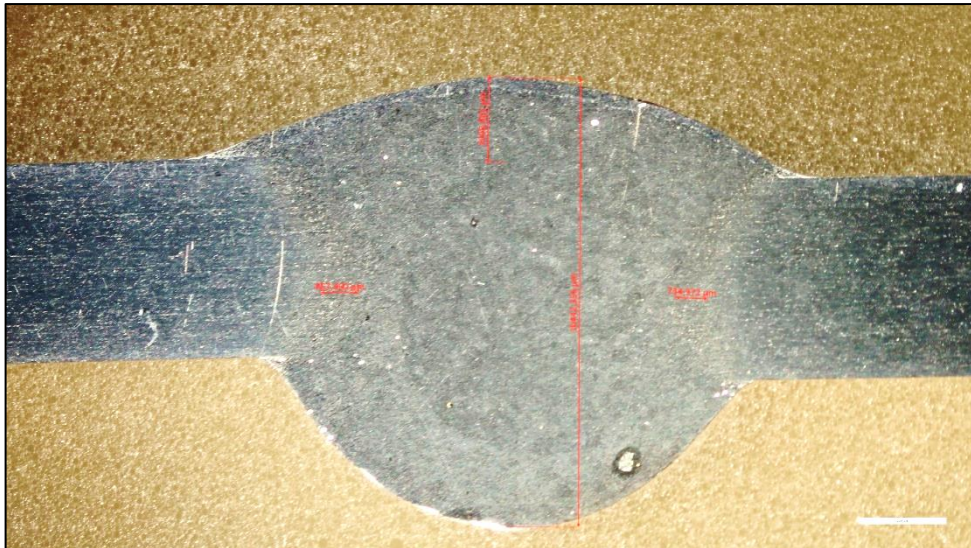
Vzorek určený pro analýzu makrostruktury.
